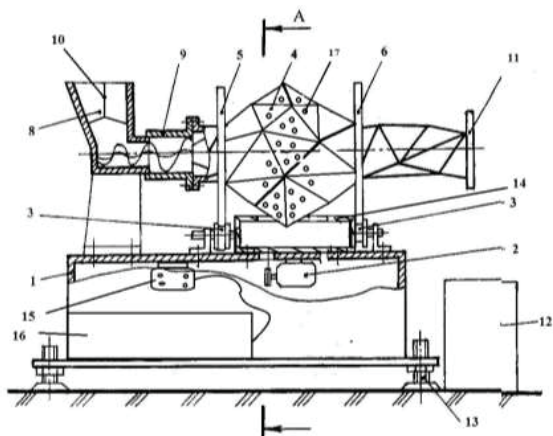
Схема установки винтового барабана (вид спереди)
